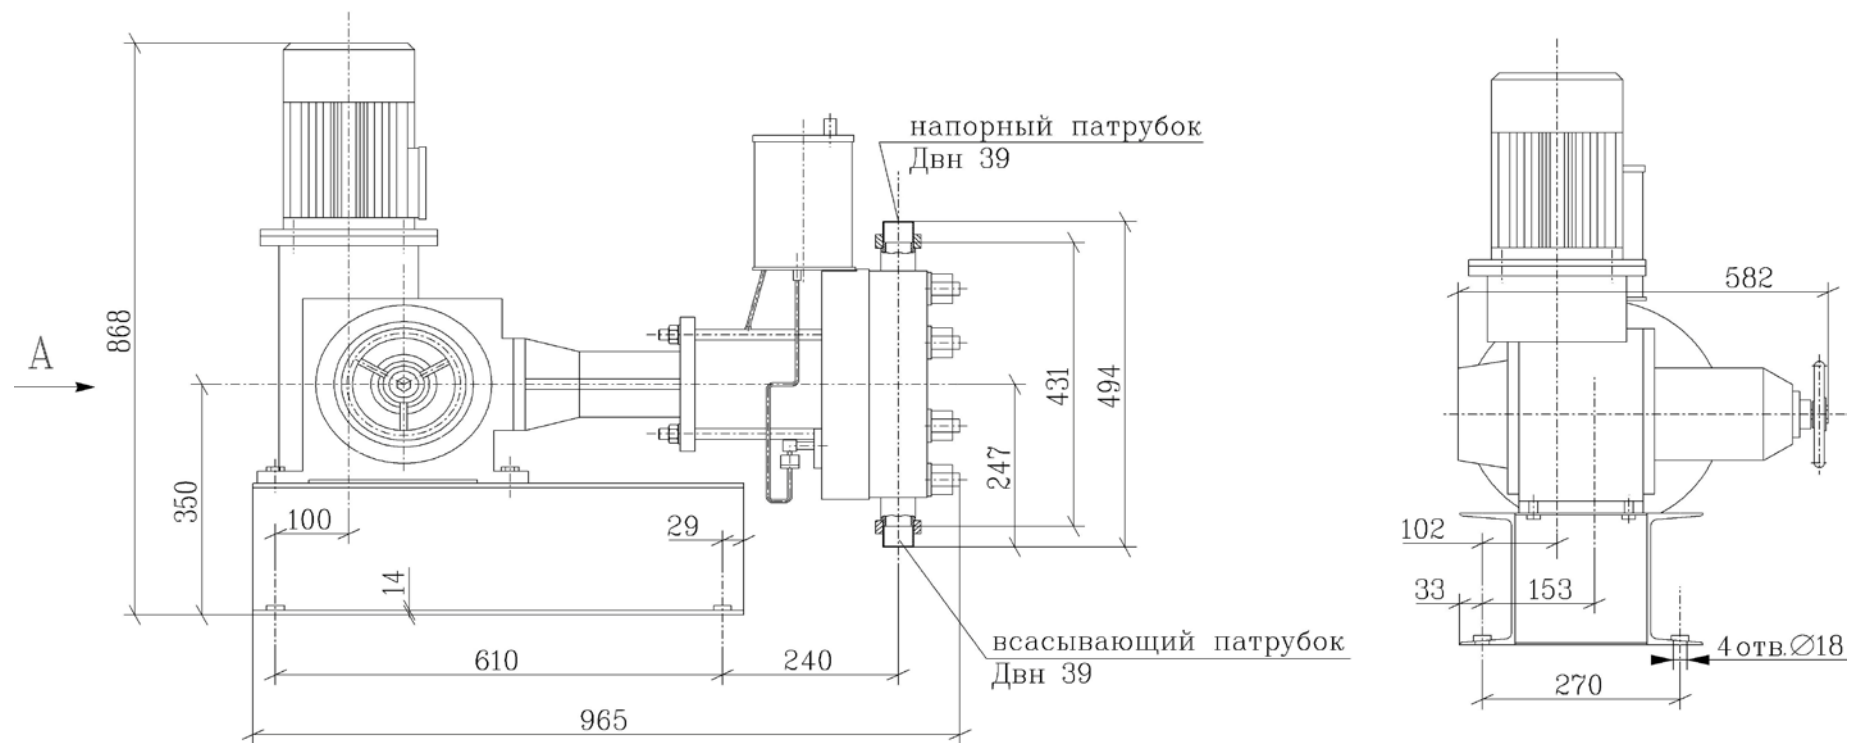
Габаритный чертеж насоса-дозатора кислоты LDP30AP001, LDP30AP002
